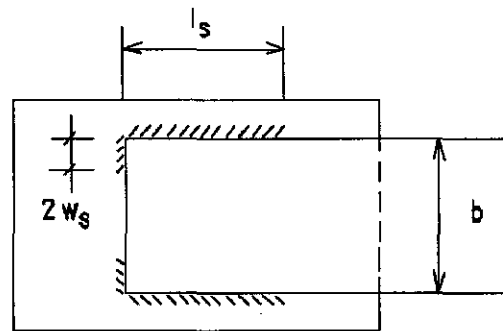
Remates de extremo en soldadura tipo filete
